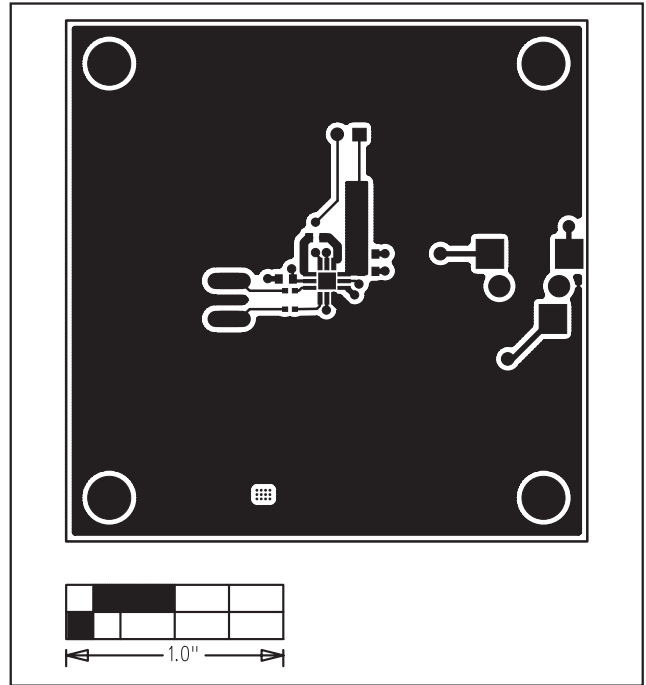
MAX9721 EV 키트 PCB 보드 레이아웃 — 부품 측
